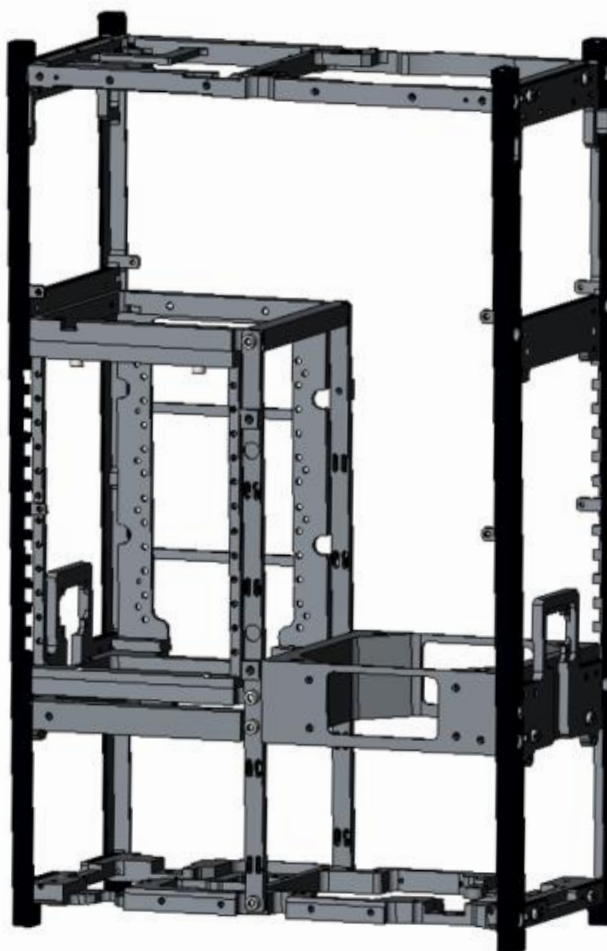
Корпус платформы на базе типа SXC6
